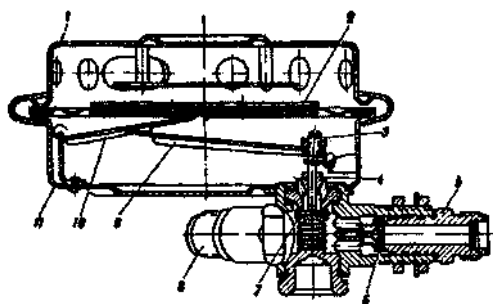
Дыхательный автомат аппарата АВМ-3: 1 — крышка, 2 — мембрана, 3 — регулировочный винт, 4 — седло клапана, 5 — подводящий штуцер, 6 — фильтр, 7 — клапан автомата, 8 — штуцер водолазного шланга, 9 — нижний рычаг, 10 — верхний рычаг, 11 — корпус автомата
